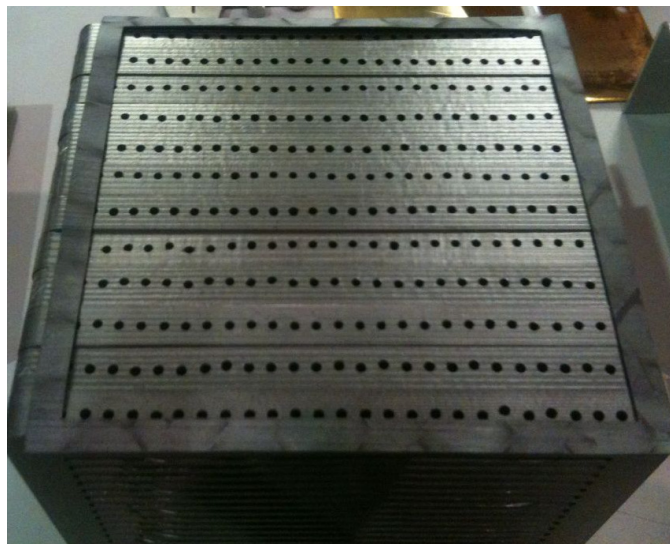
Seitenansicht mit aufgelegter Laser cut Dichtung
